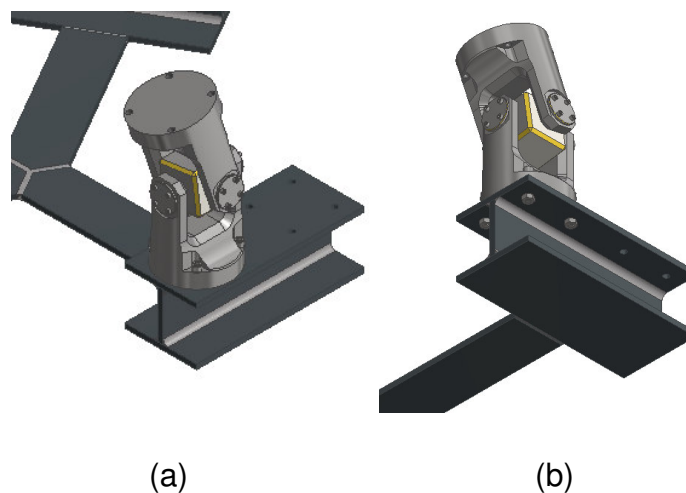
Ensamblaje de la junta inferior a la base fija
